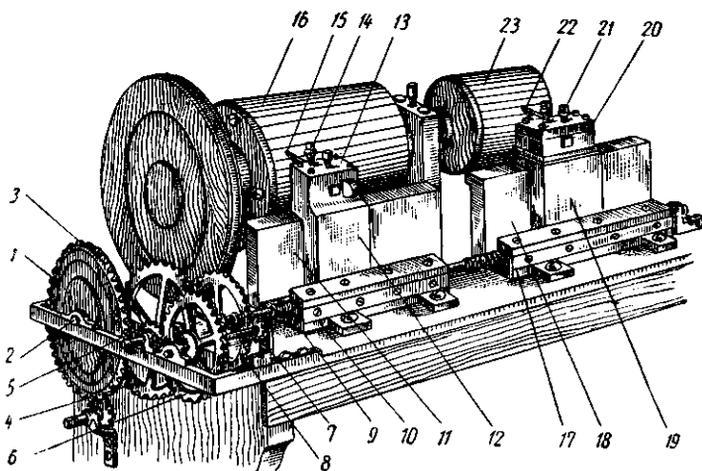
Супорт токарно-копировального станка Яковлева—Нартова.
